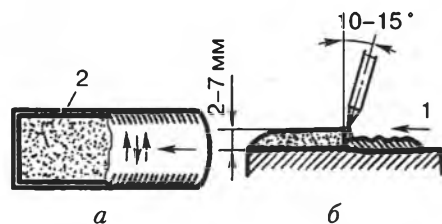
Положення вугільного електрода при наплавленні порошокоподібних твердих сплавів: а — переміщення електрода; б — вид збоку; 1 (стрілка) — загальний напрям наплавлення; 2 — шар шихти (порошку)
